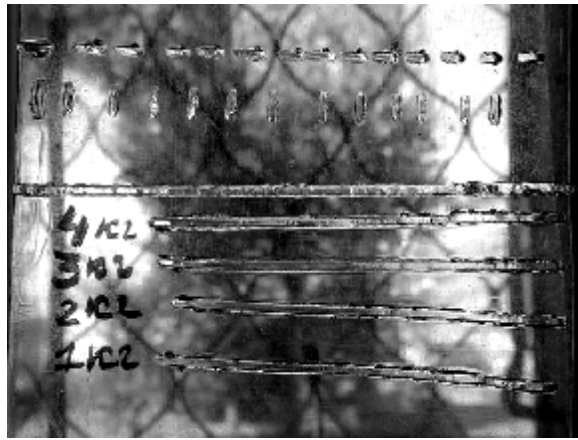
Шов после процесса непрерывной ультразвуковой сварки
